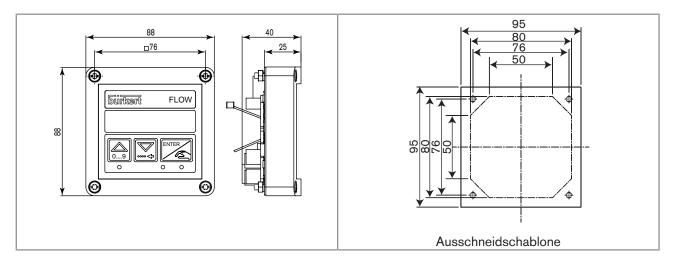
Abmessungen des Transmitters 8025 Universal, Schaltschrank-Ausführung, und der Ausschneidschablone [mm]
